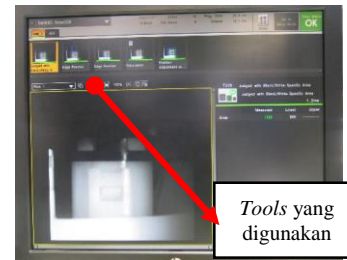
Mesin *Cut Valve Leak Inspection* Setelah Ditambahkan *Smart Camera Unit
